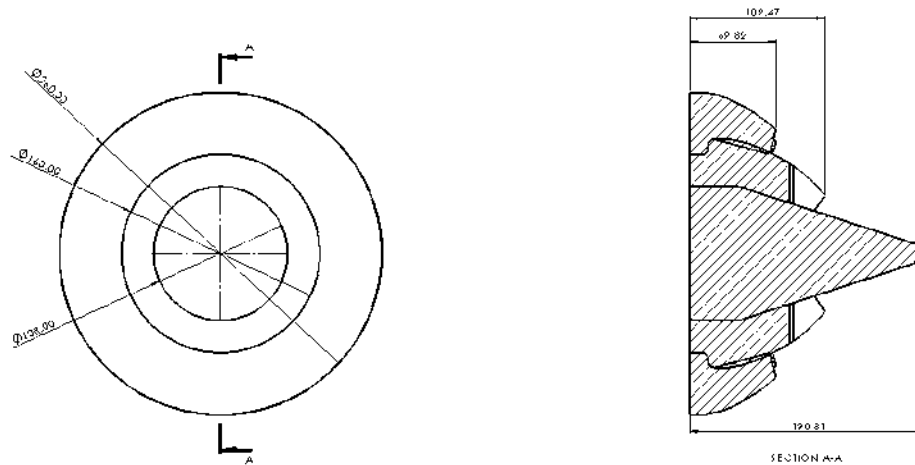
Plano de diseño CAD 2 (E14I8). [Autoría propia]
